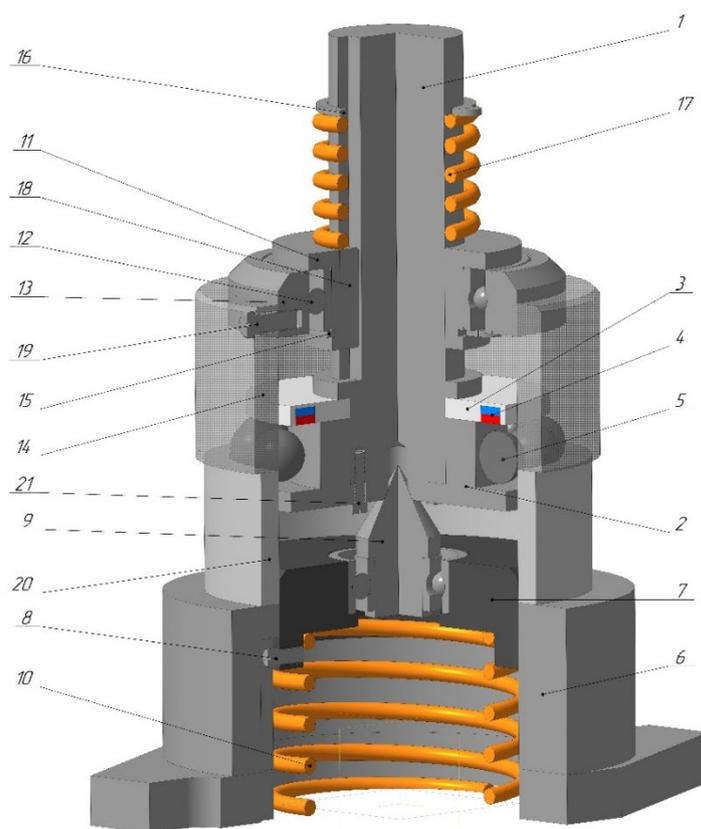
Конструкция устройства для поверхностного пластического деформирования внутренней поверхности нежесткой втулки
